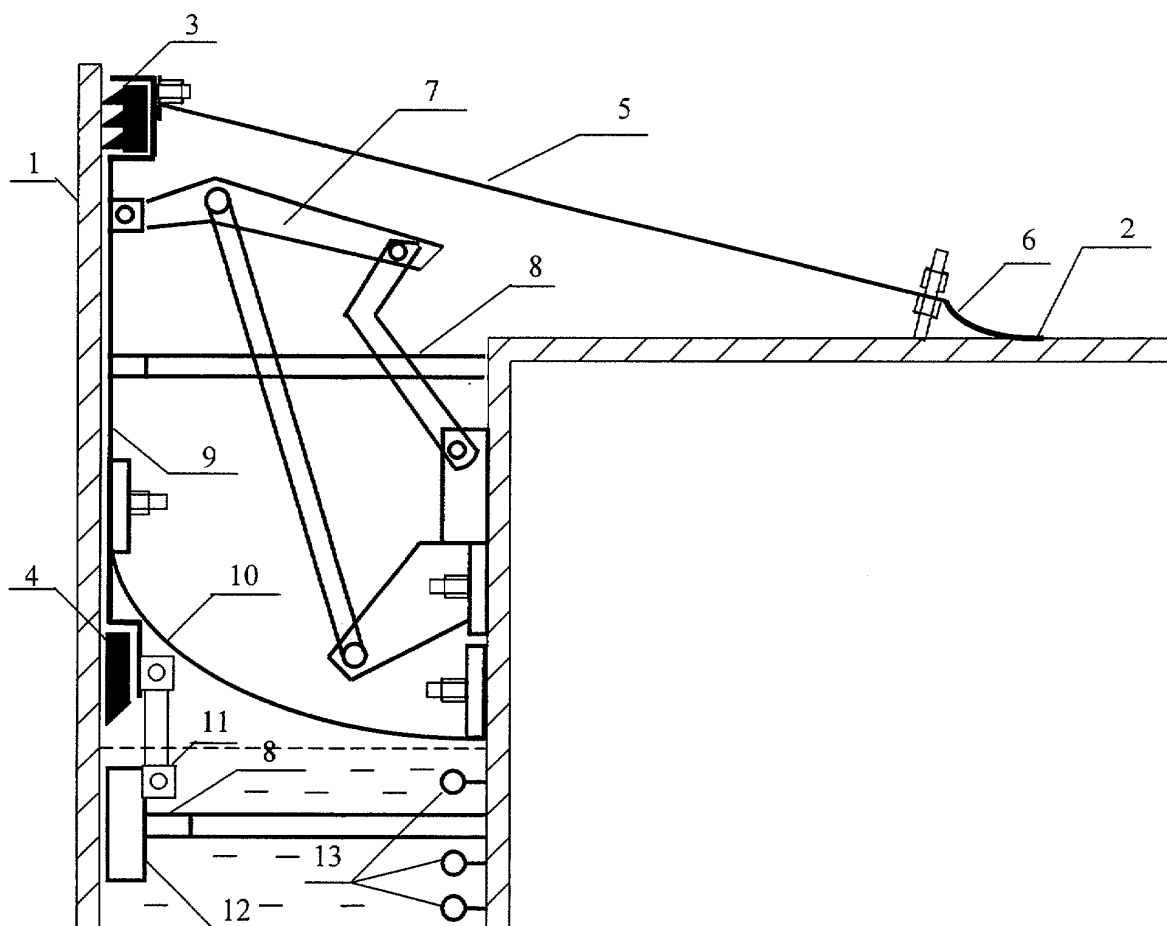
Общий вид уплотняющего затвора плавающих крыш.
